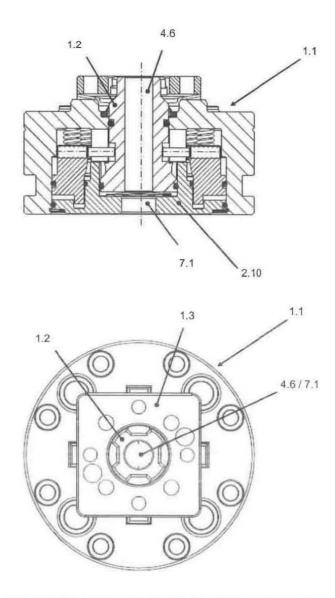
Versión hueca del mandril de apriete; vista lateral y en planta superior
